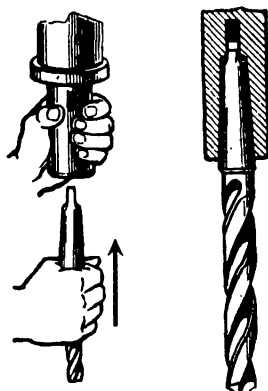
Закрепление инструмента непосредственно в шпинделе станка
